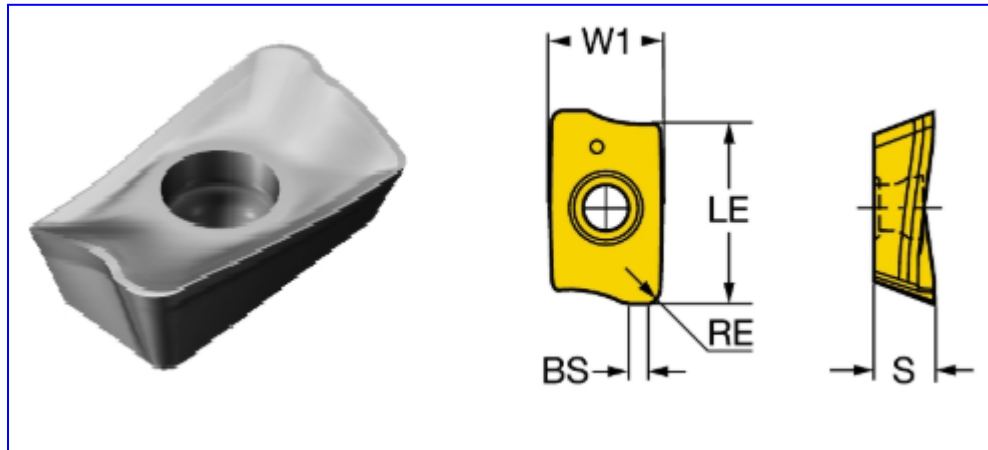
La géométrie de l'outil fraise et de la plaquette.
